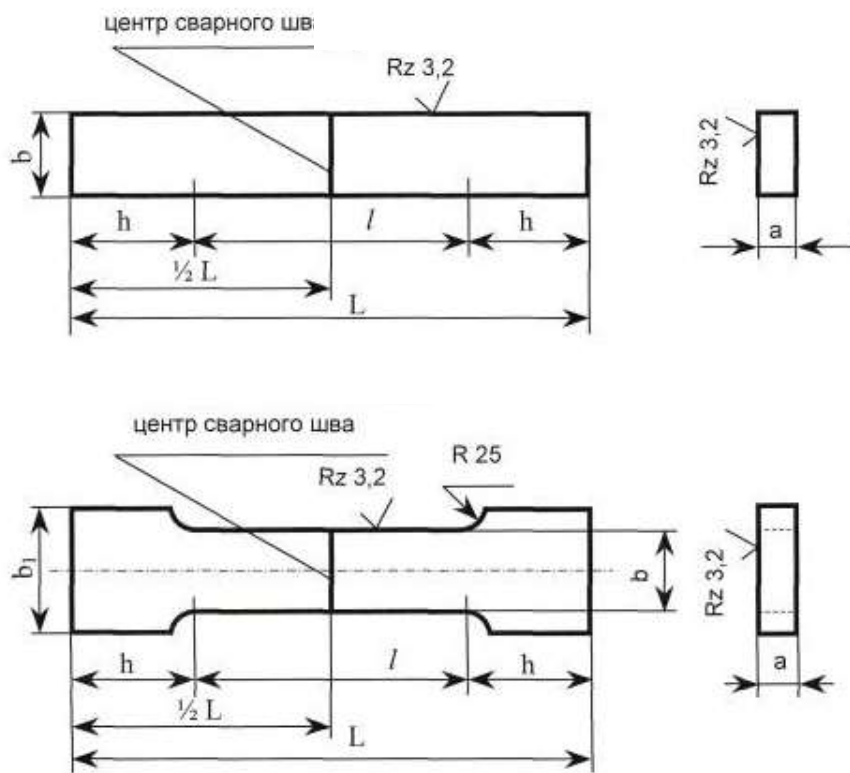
Форма и размеры образцов для испытаний сварного соединения на статическое растяжение
